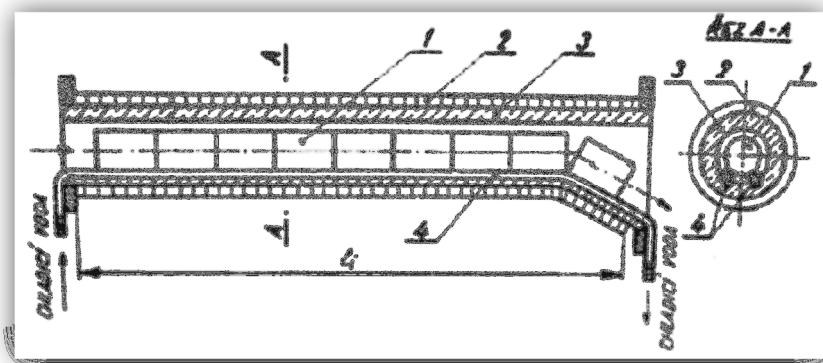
Kanálková indukční pec LINEMELT [22]
